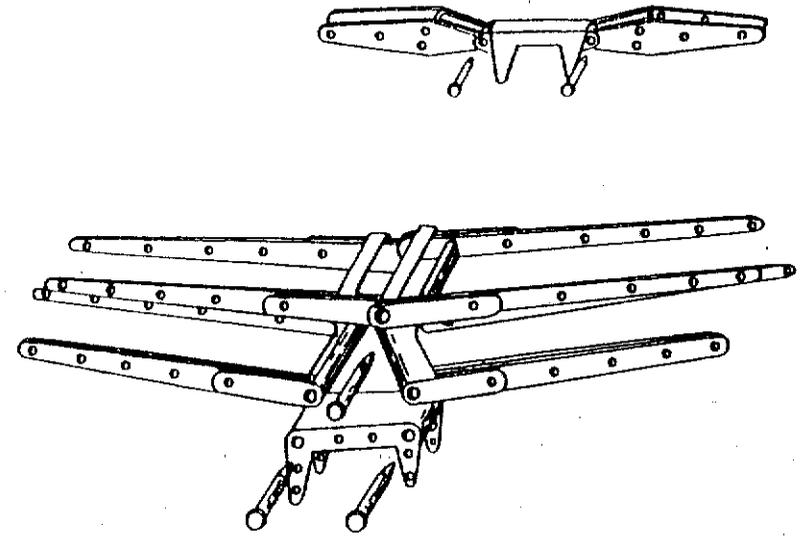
Ensemble des ferrures de fixation d'ailes en porte à faux.
